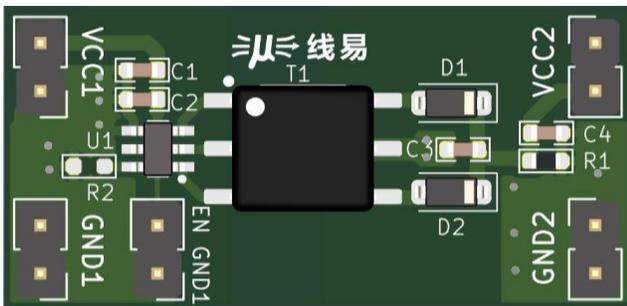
PCB 版图正面(尺寸: 16x 33 mm)
